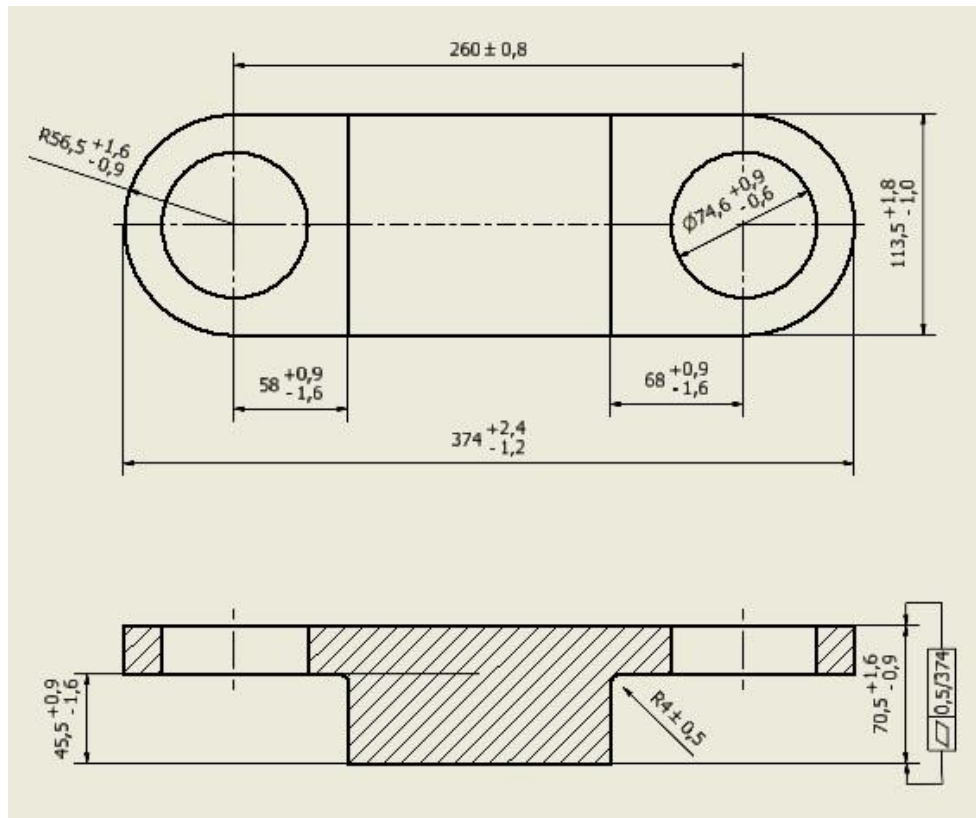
Ескіз проектної заготовки, (поковка)
